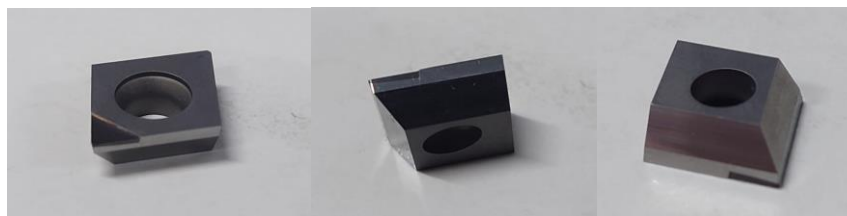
Режущая пластина ПКА с задними углами (11° и 29°)
